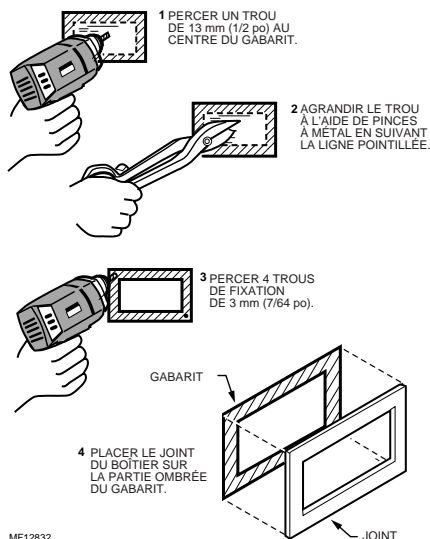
Utiliser le gabarit pour installer le régulateur.
